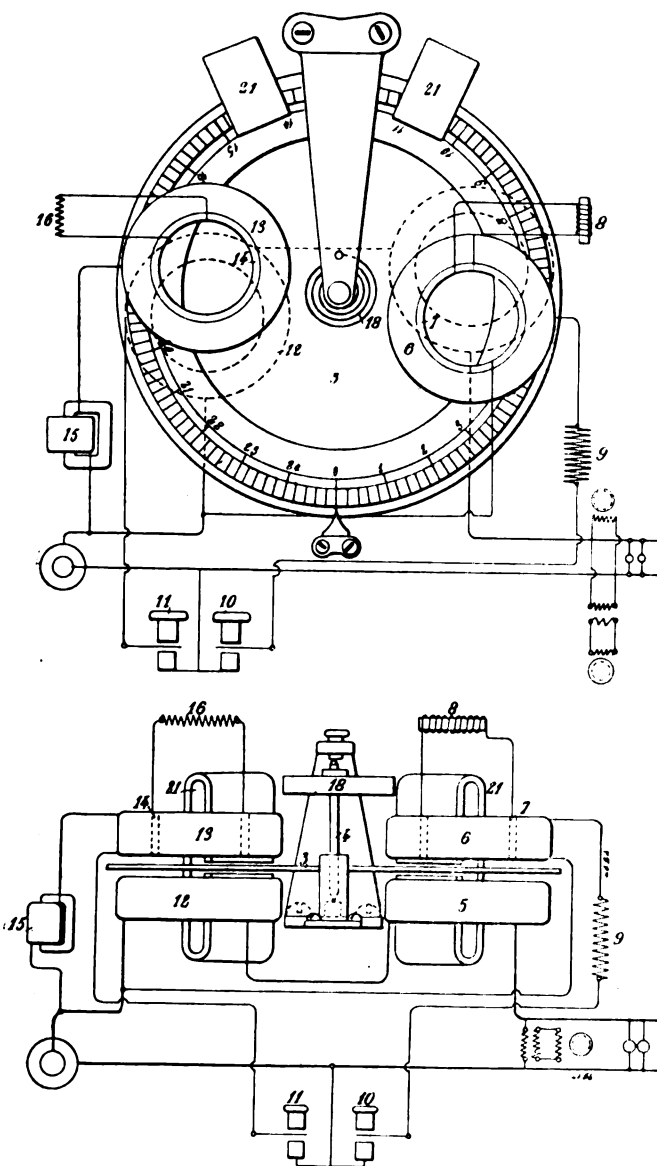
et 2. — Plan et élévation du wattmètre Duncan.
